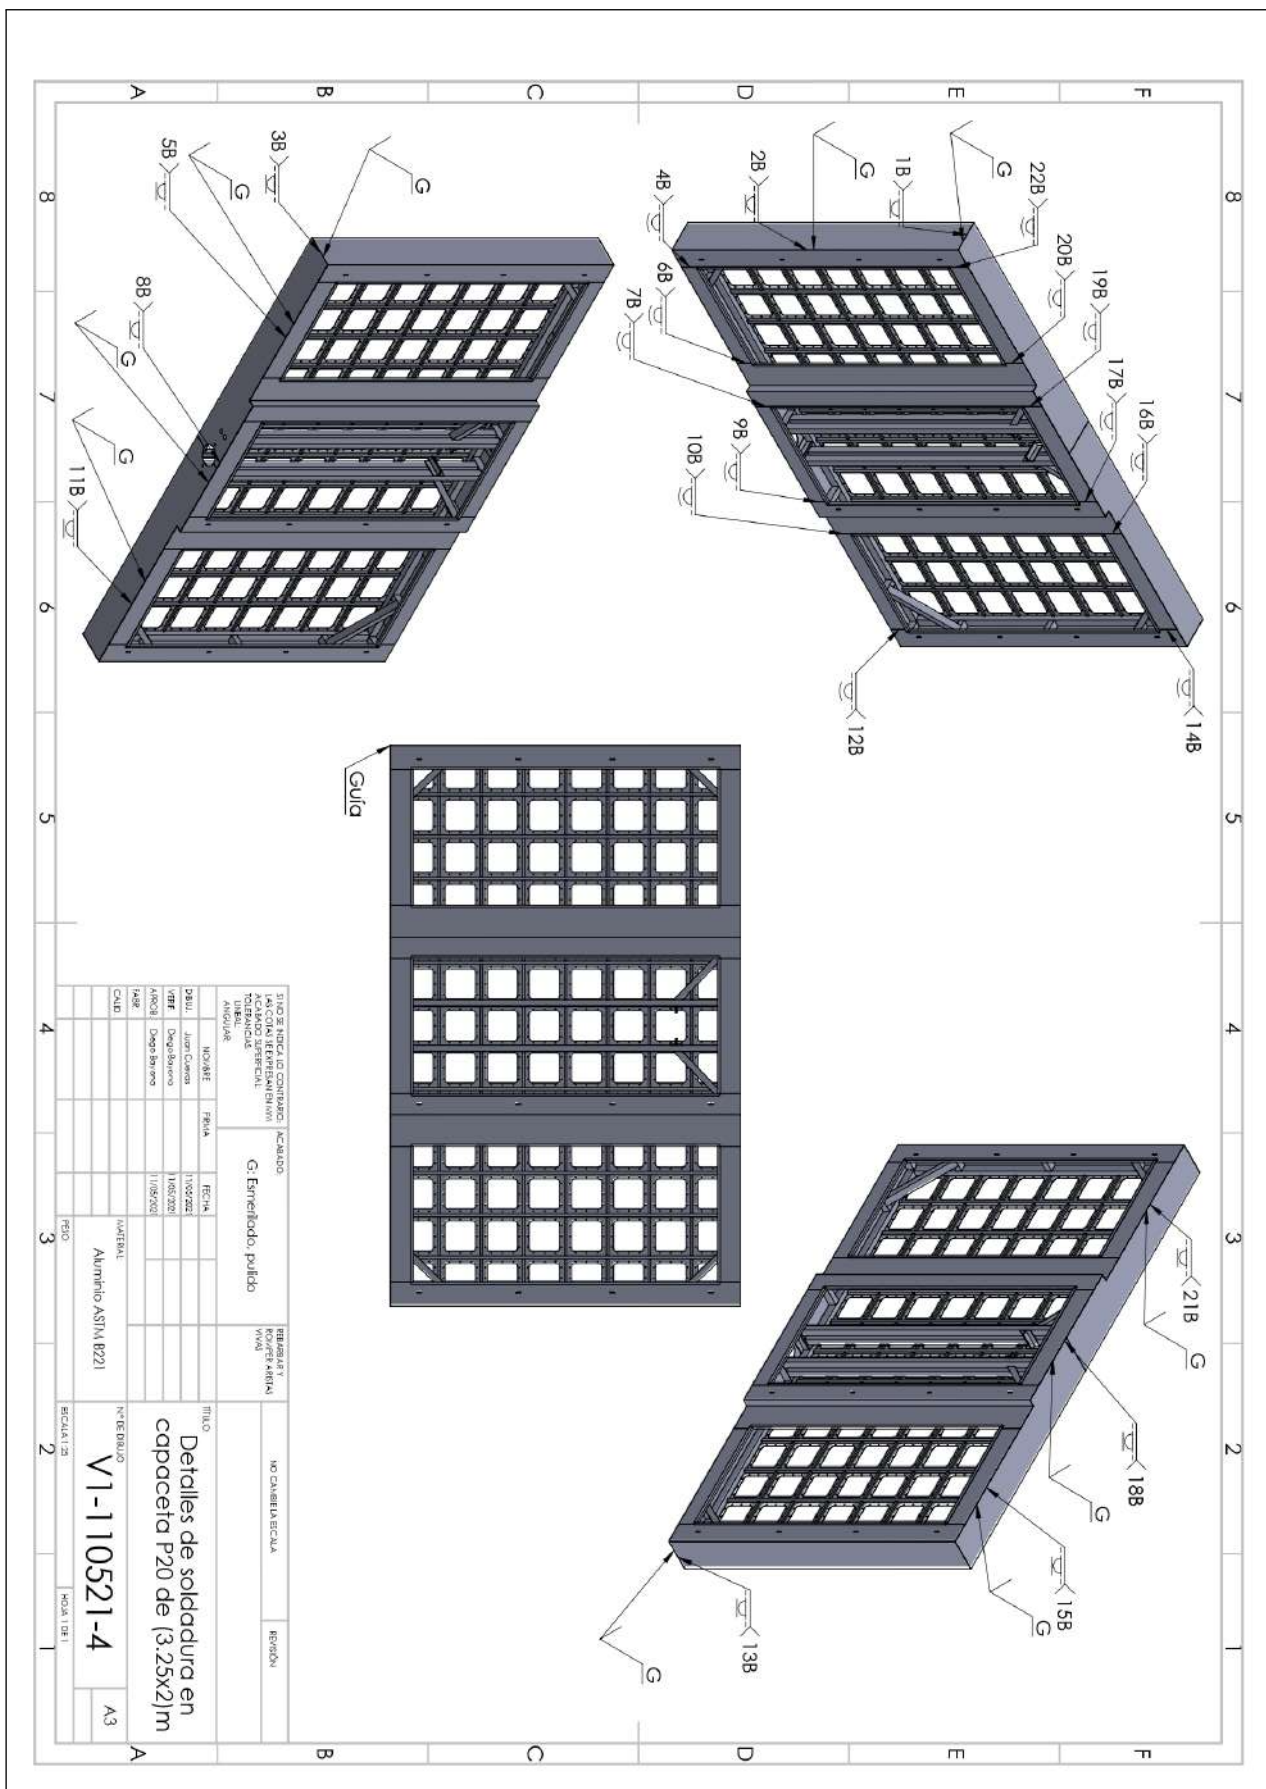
Detalles de soldadura en capaceta P20 uniones B.
